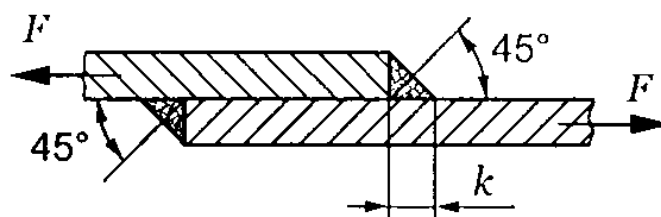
Схема на пускового зварного з'єднання.
